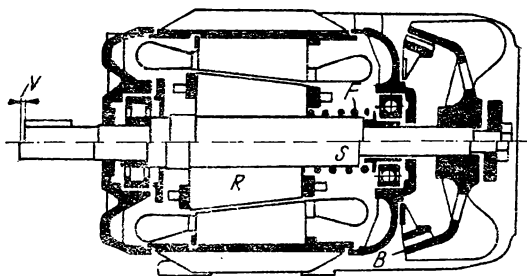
Frinarea motorului asincron cu rotor tronconic.
